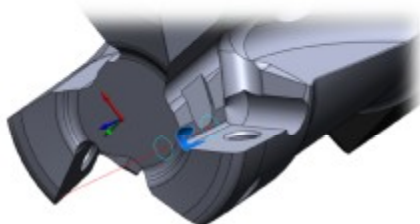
Operace 3 – vygenerované dráhy a obrobení
